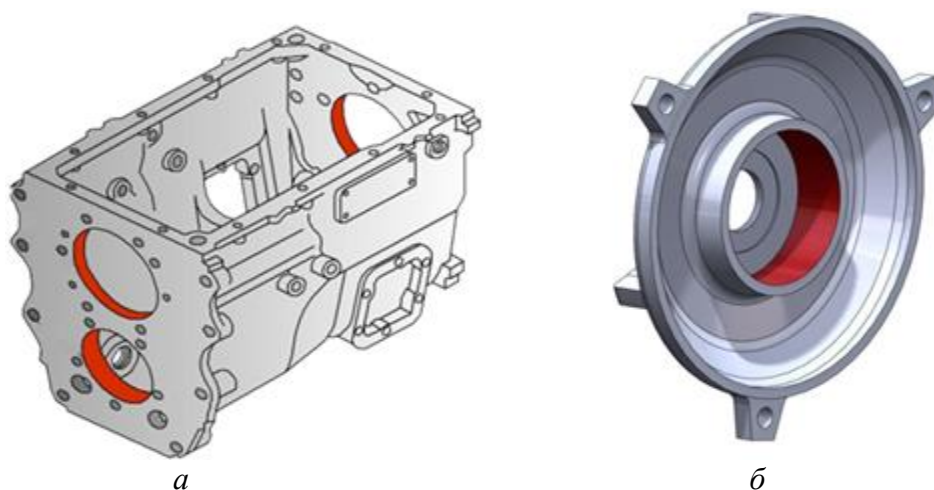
Посадочные отверстия в корпусных деталях автомобиля, восстановленные нанесением полимерного покрытия: *а* – корпус коробки передач автомобиля; *б* – подшипниковый щит генератора автомобиля
